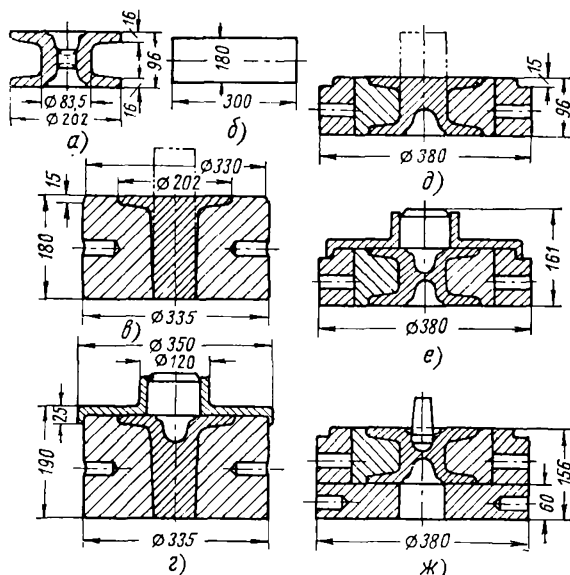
Изготовление поковки ступицы в подкладном штампе: а — поковка ступицы; б — исходная заготовка; в, г, д, е — этапыковки ступицы; ж — прошивка отверстия
